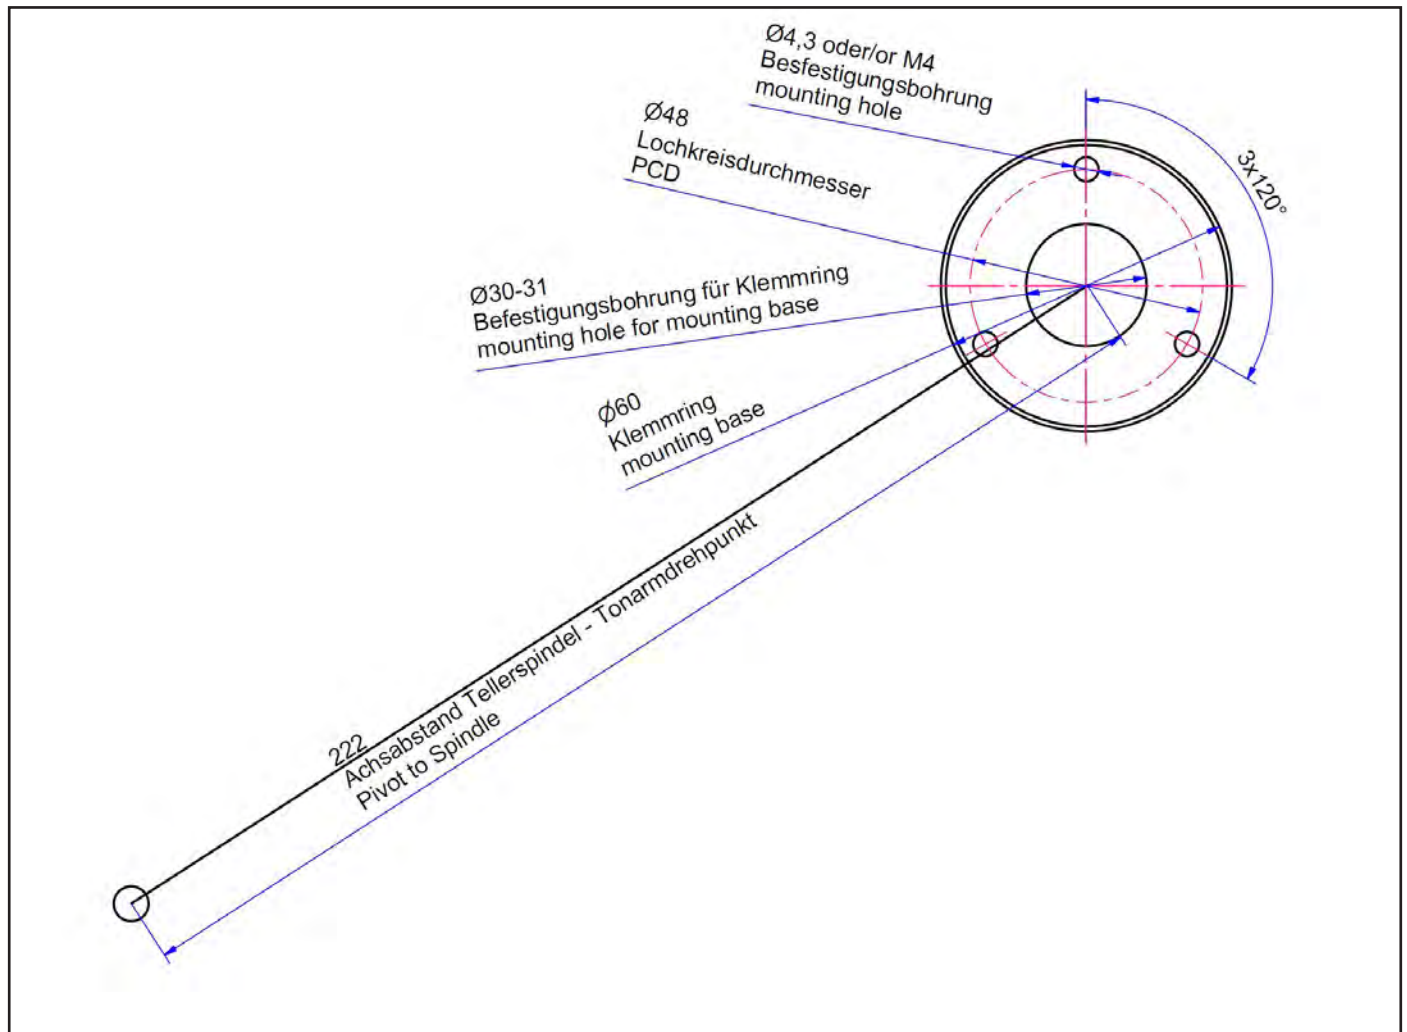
Montage des Klemmrings auf einem Laufwerk anderer Hersteller
